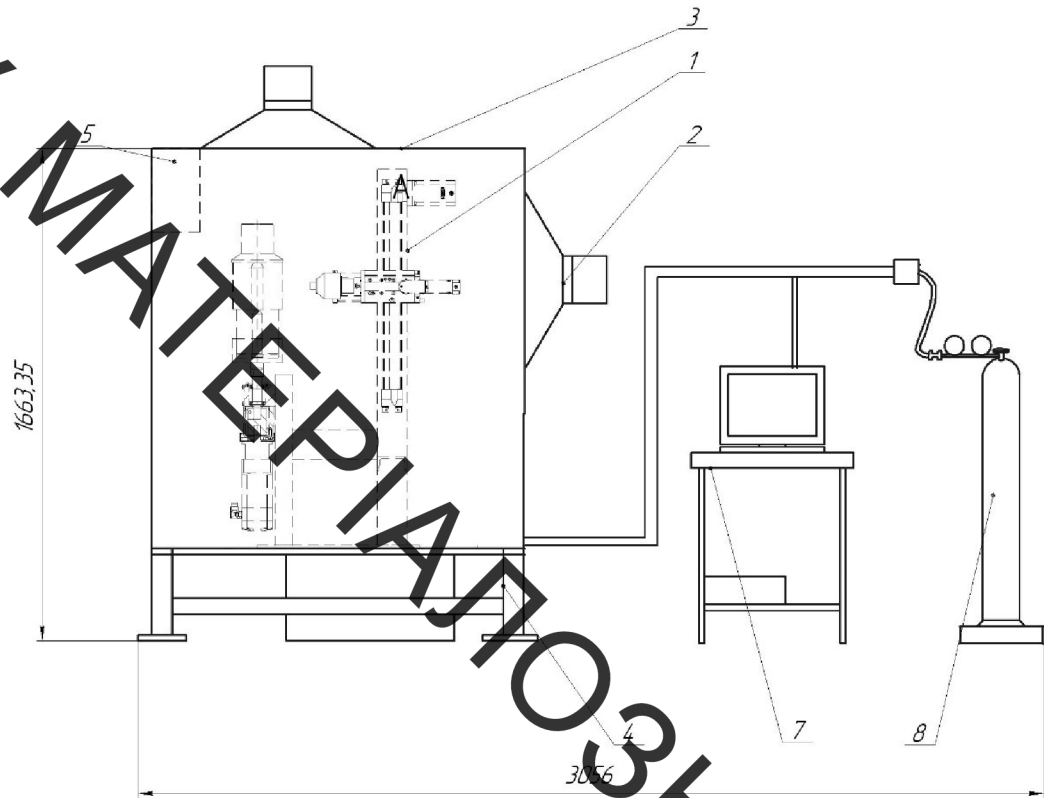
Робоче місце для наплення валу 4-ої передачі редуктора СПЦ26У: 1–установка з ЧПК, 2–вентиляція, 3–Камера захисна, 4– станина, 5–механізм подачі порошку, 6–блок живлення, 7–комп'ютер, 8–балон
